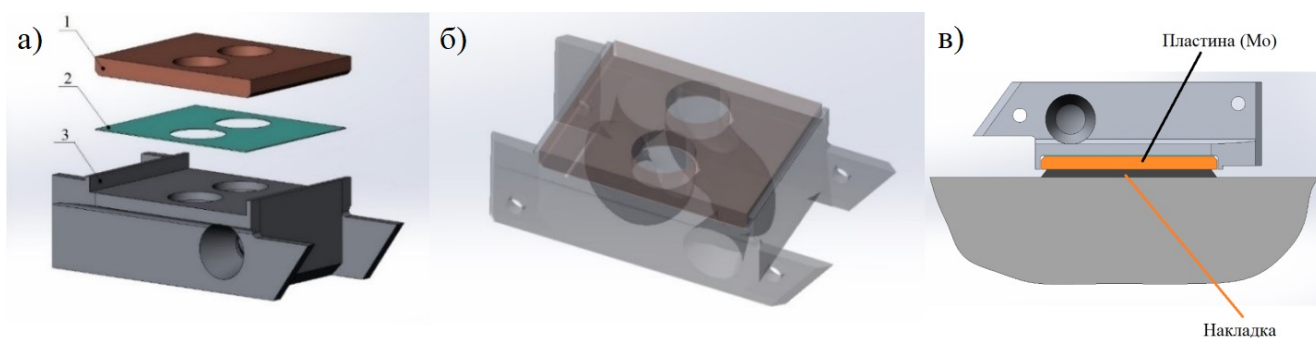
Составные части детали «Корпус» (а), внешний и внутренний контур детали (б), рабочее положение детали (в)
